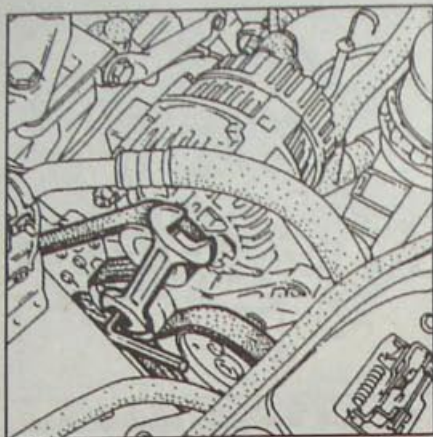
Использование шестигранного и рожкового ключа для поворота натяжного ролика (1) и ослабления натяжения приводного ремня насоса усилителя рулевого управления
